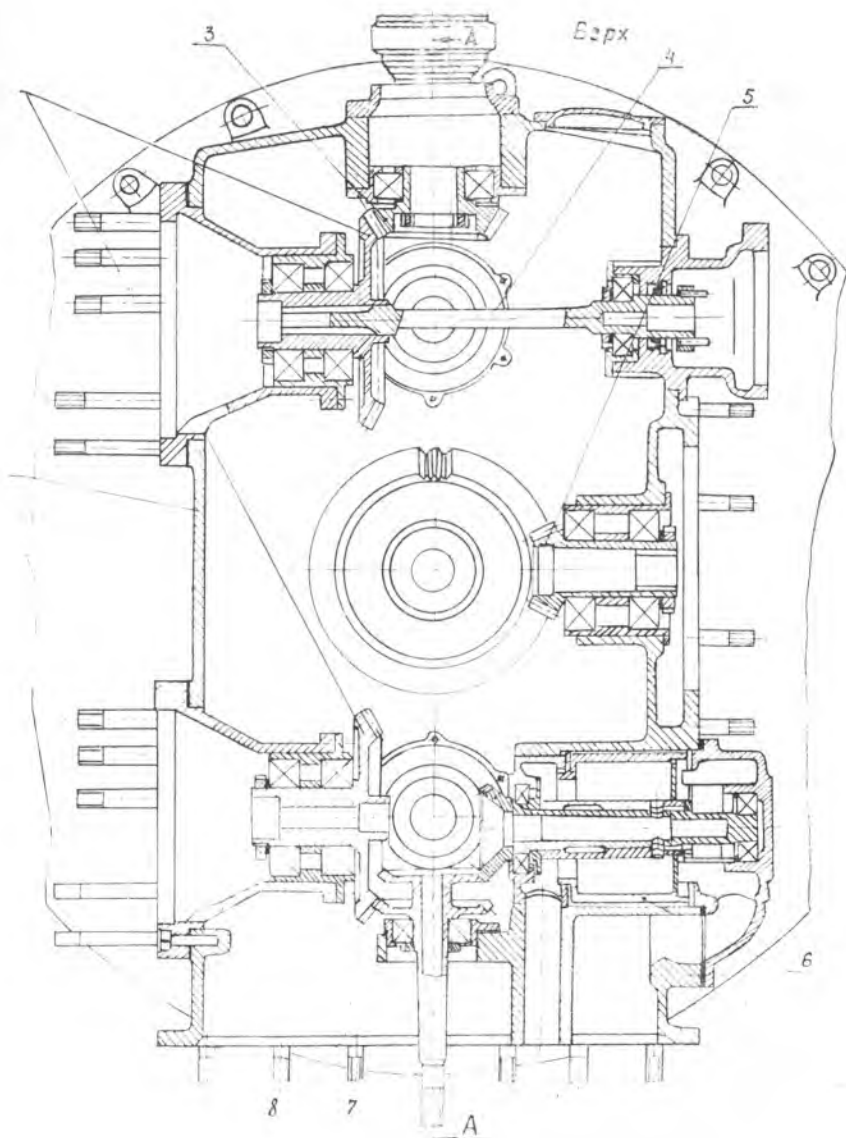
Конструкция коробки приводов агрегатов: 1 — корпус; 2 — коническое колесо запасного привода; 4 — рессора привода тахометра; 7 — ведомое коническое колесо привода маслонасоса; 8 — ведомое колесо верхнее; 10—ведущее коническое колесо верхнее; 11—ведомое механизм; 14 — рессора; 15 — ведущее цилиндрическое колесо; 16 — колесо нижнее; 18 — втулка суфлера; 19—гайка;
